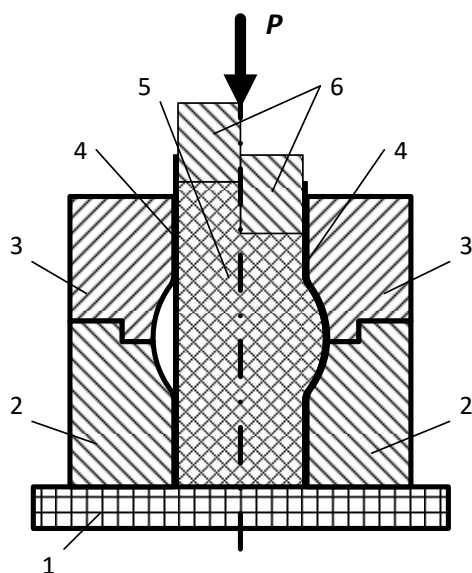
Схема раздачи трубчатой заготовки с использованием внутреннего наполнителя
